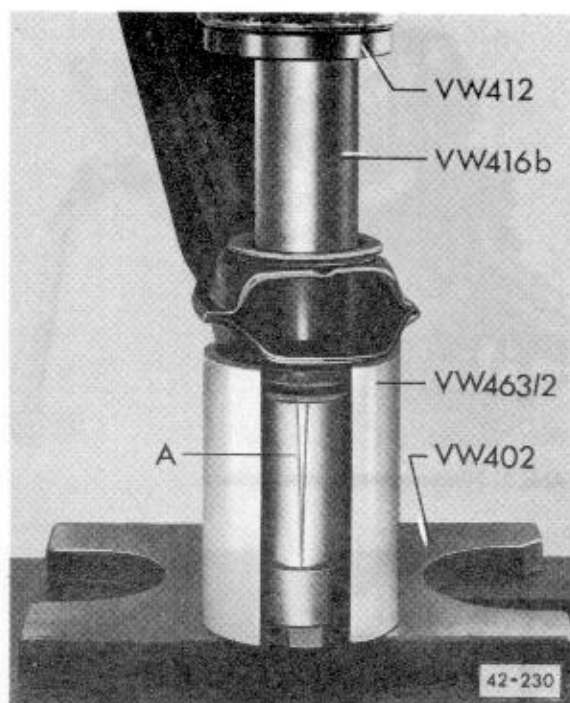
Äußere Buchse der Gummimetallager auspressen
